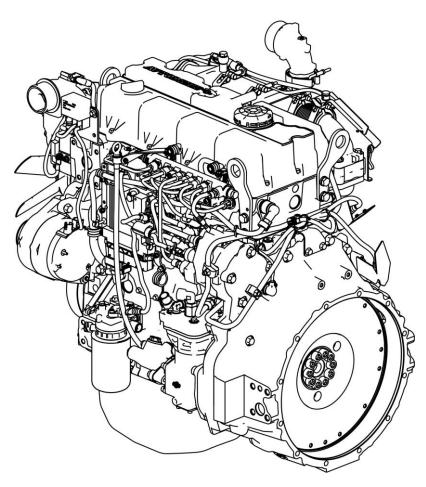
а – Двигатель ЯМЗ-53443-30 (общий вид слева)
